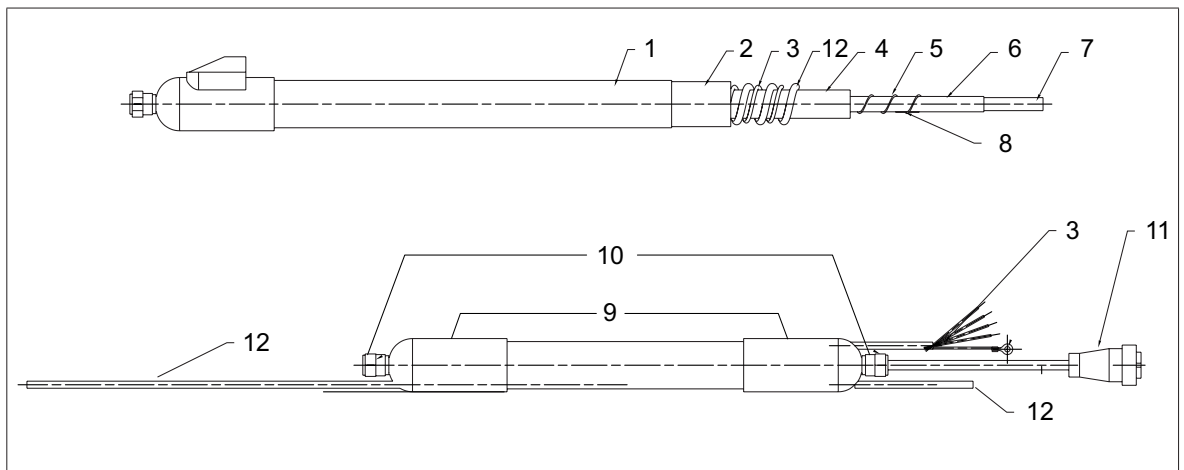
/6: Mechanische montage van de slang (versie spray)
